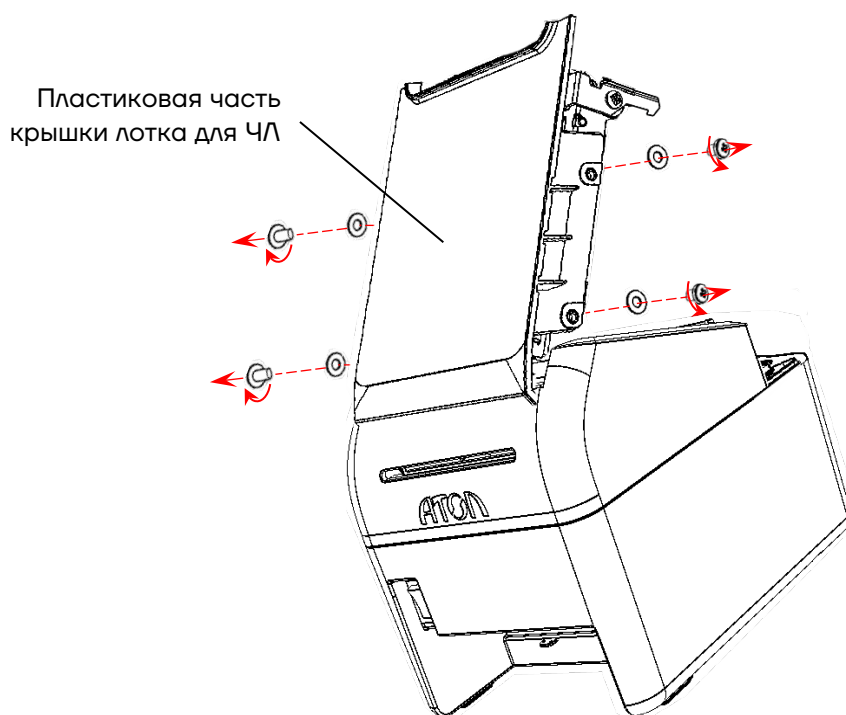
Элементы крепления пластиковой части крышки лотка для ЧЛ к металлической раме печатающего механизма
